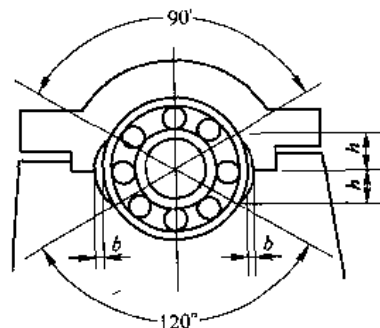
轴承外圈与轴承底座、轴承盖接触面的角度
